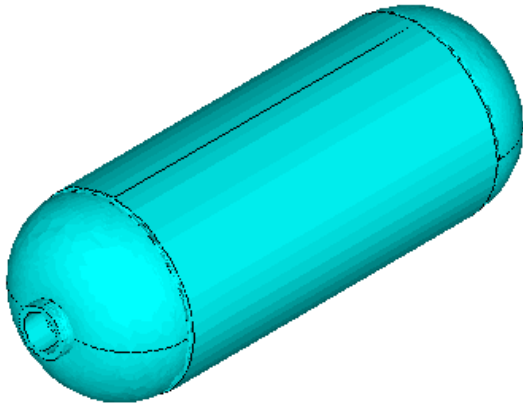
Модель лайнера малогабаритного корпуса
